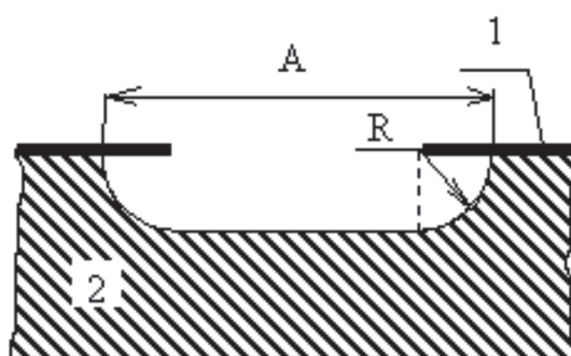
Травлення металічної заготовки під покриттям: 1 – покриття; 2 – заготовка
